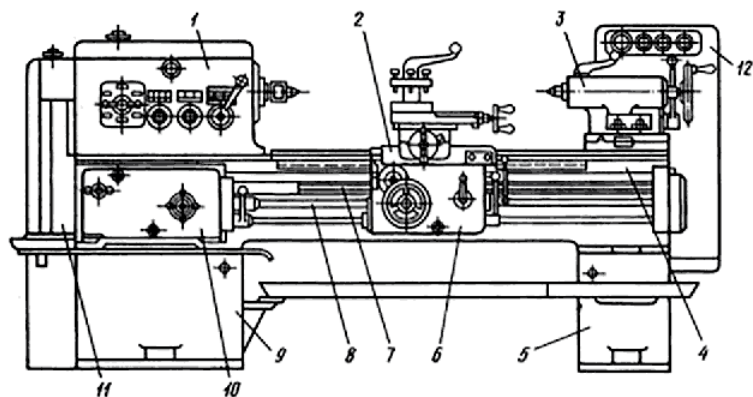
Сборочные единицы (узлы) и механизмы токарно-винторезного станка:
